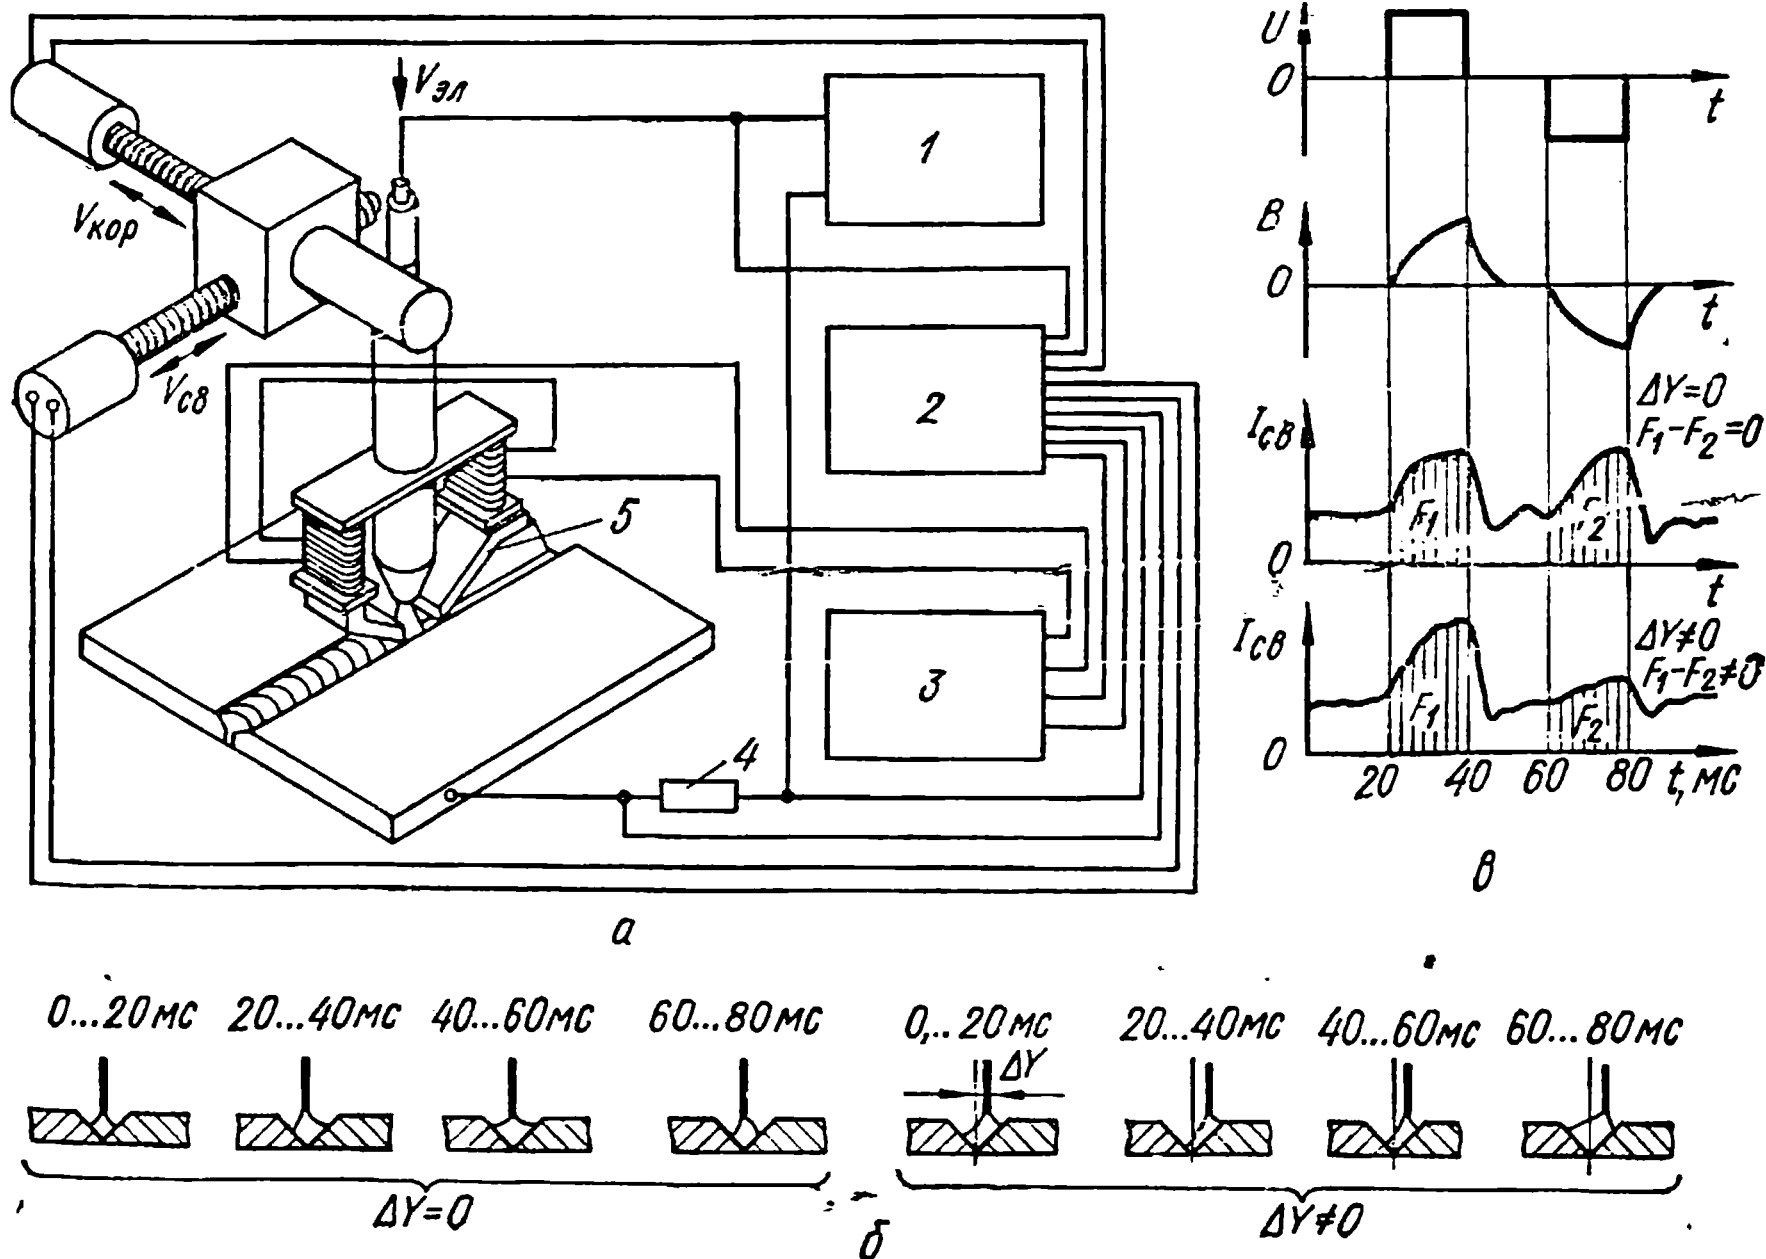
Система со сканированием сварочной дугой:
